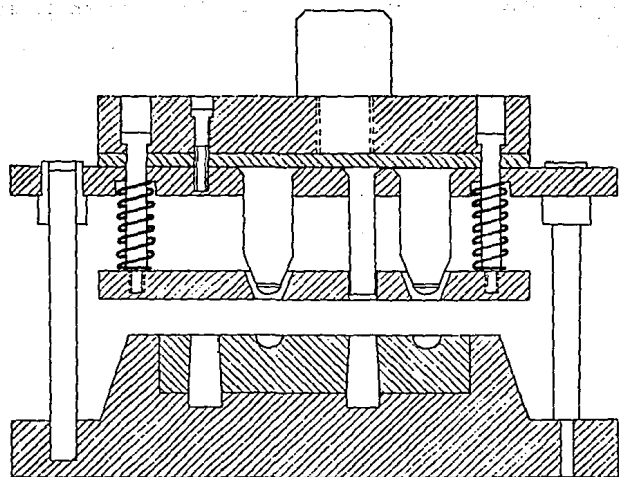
Esquema final del troquel para estampar casquillas.
